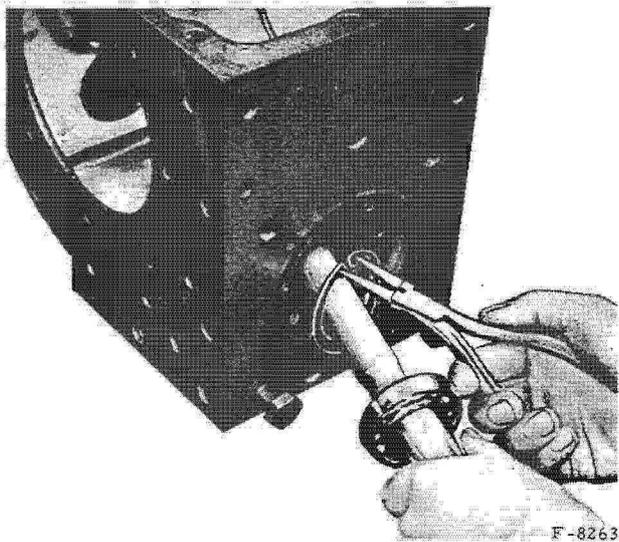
Circlip arrière du roulement d'arbre de prise de force.
